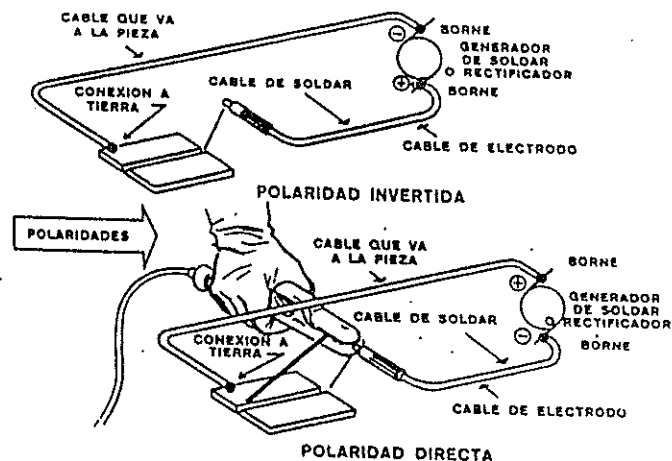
Equipo de soldadura con electrodo revestido.
